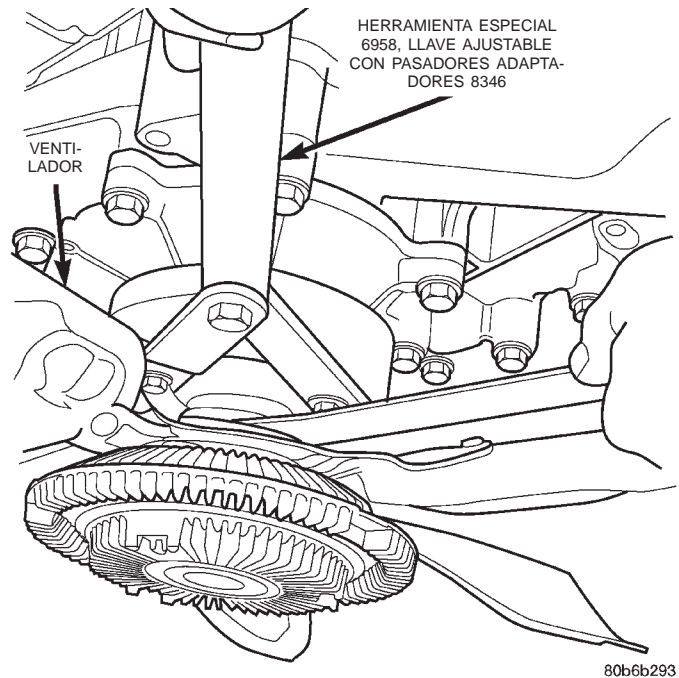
Ventilador de transmisión viscosa, motor 4.7L
